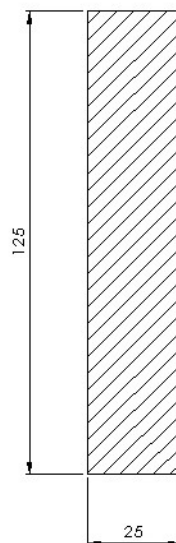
Sección rectangular de viga horizontal con dimensiones en mm (Fuente: propia)
